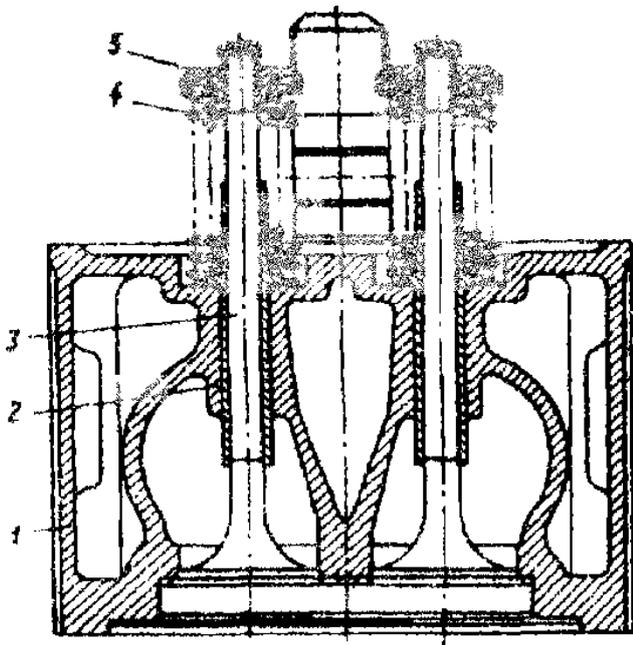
Расположение клапанов на головке цилиндра дизеля Ч 12/14:
